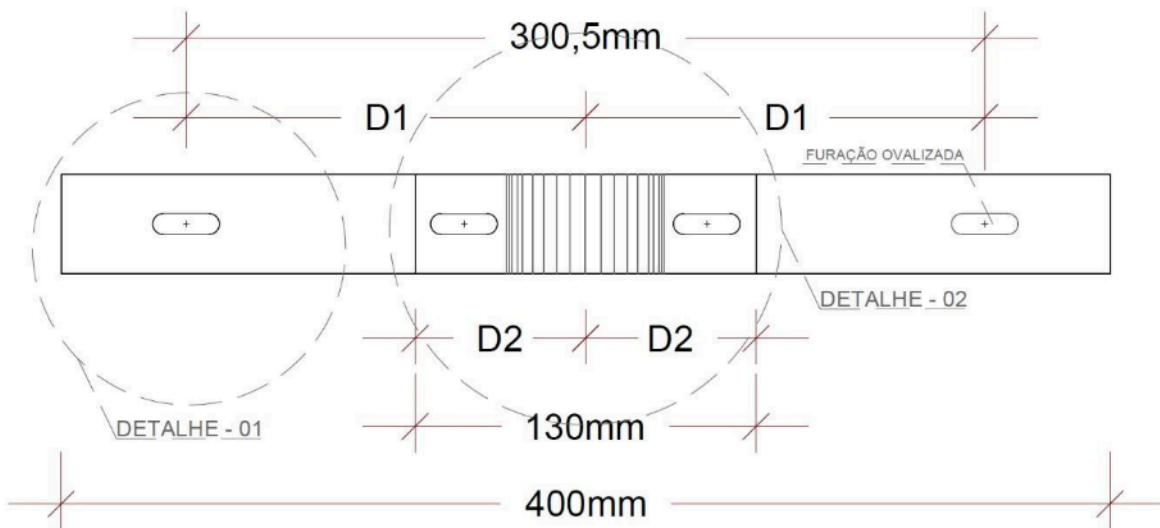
VISTA POSTERIOR DA ABRAÇADEIRA. FONTE: DET/SMST/PMBV
